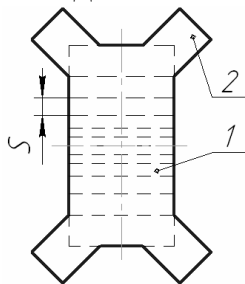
Эскиз исходной прессованной заготовки для отбора образцов под прокатку:
